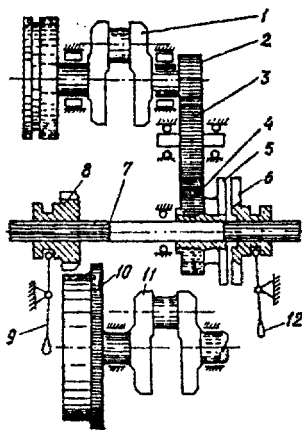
Схема трансмиссии пускового двигателя: 1 — коленчатый вал пускового двигателя; 2, 3 и 4 — шестерни понижающей передачи; 5 — ведущий диск сцепления; 6 — ведомый диск сцепления; 7 — вал; 8 — приводная шестерня; 9 — рычаг приводной шестерни; 10 — венец маховика; 11 — коленчатый вал основного двигателя; 12 — рычаг сцепления
